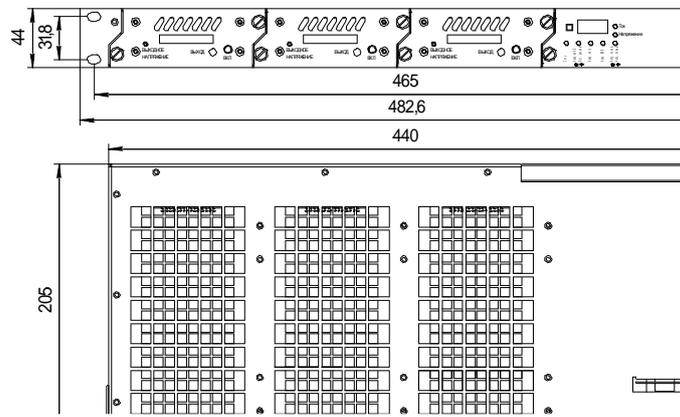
Габаритный чертеж УЭП-2К
